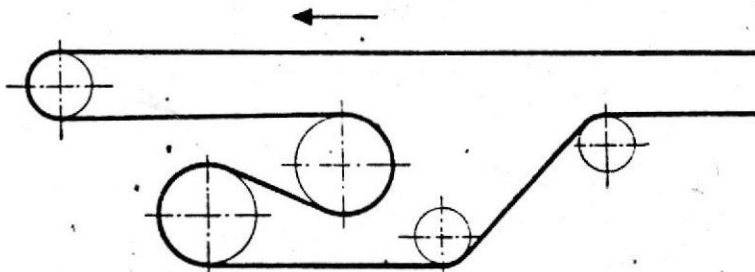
Cabeza motriz tipo tándem con accionamiento por motor único (tambores motrices enlazados por engranajes.)
